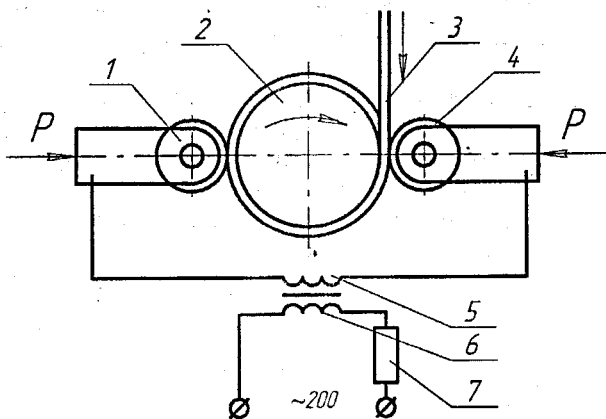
Схема електроконтактного наплавлення: 1 – контактний ролик; 2 – деталь; 3 – дріт; 4 – наплавлювальний ролик; 5 – вторинна обмотка трансформатора; 6 – первинна обмотка трансформатора; 7 – переривач струму
